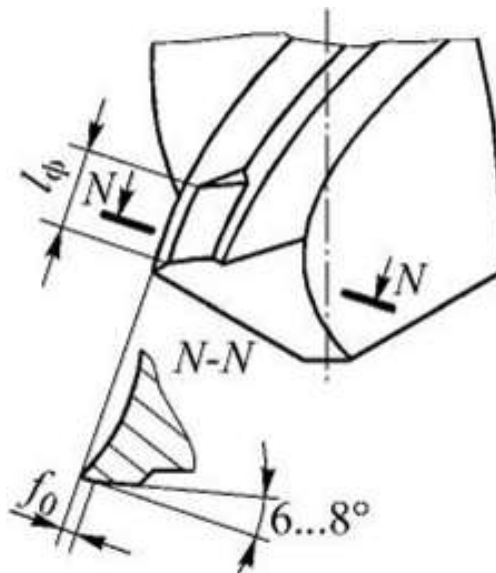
Підточування калібрувальної стрічки спірального свердла
